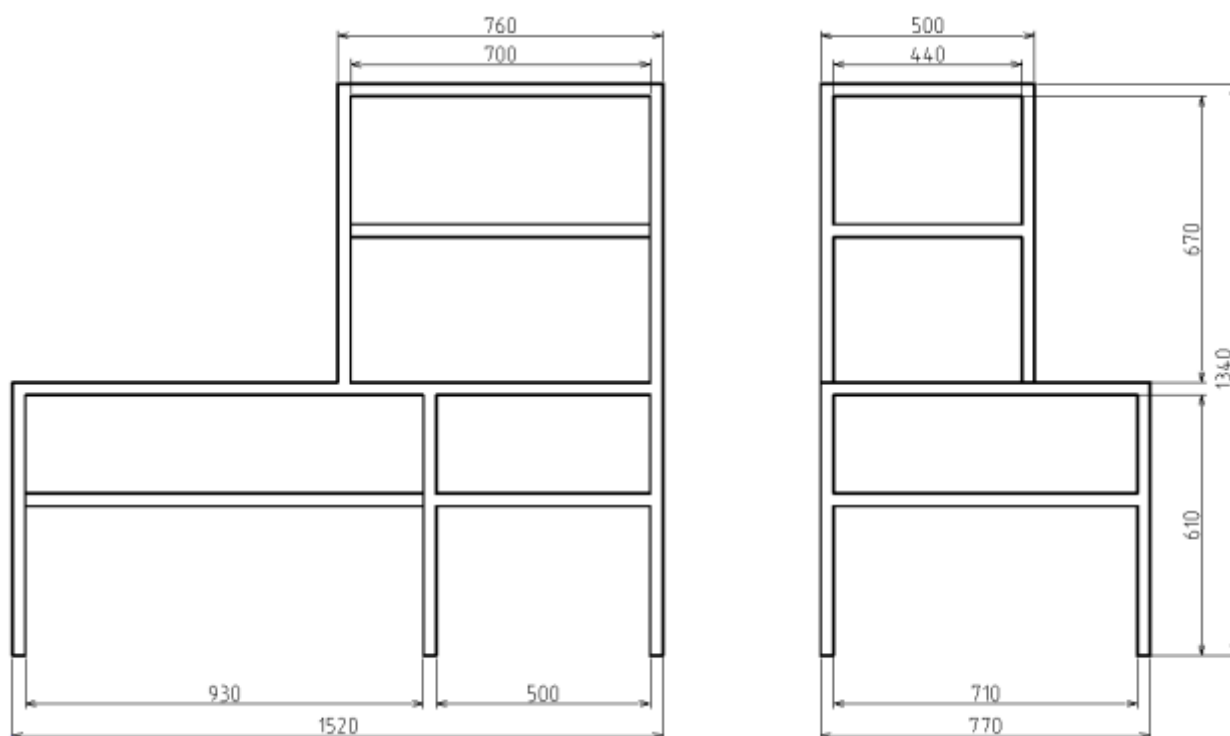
Габаритные размеры конструкции и размеры ее отделений
